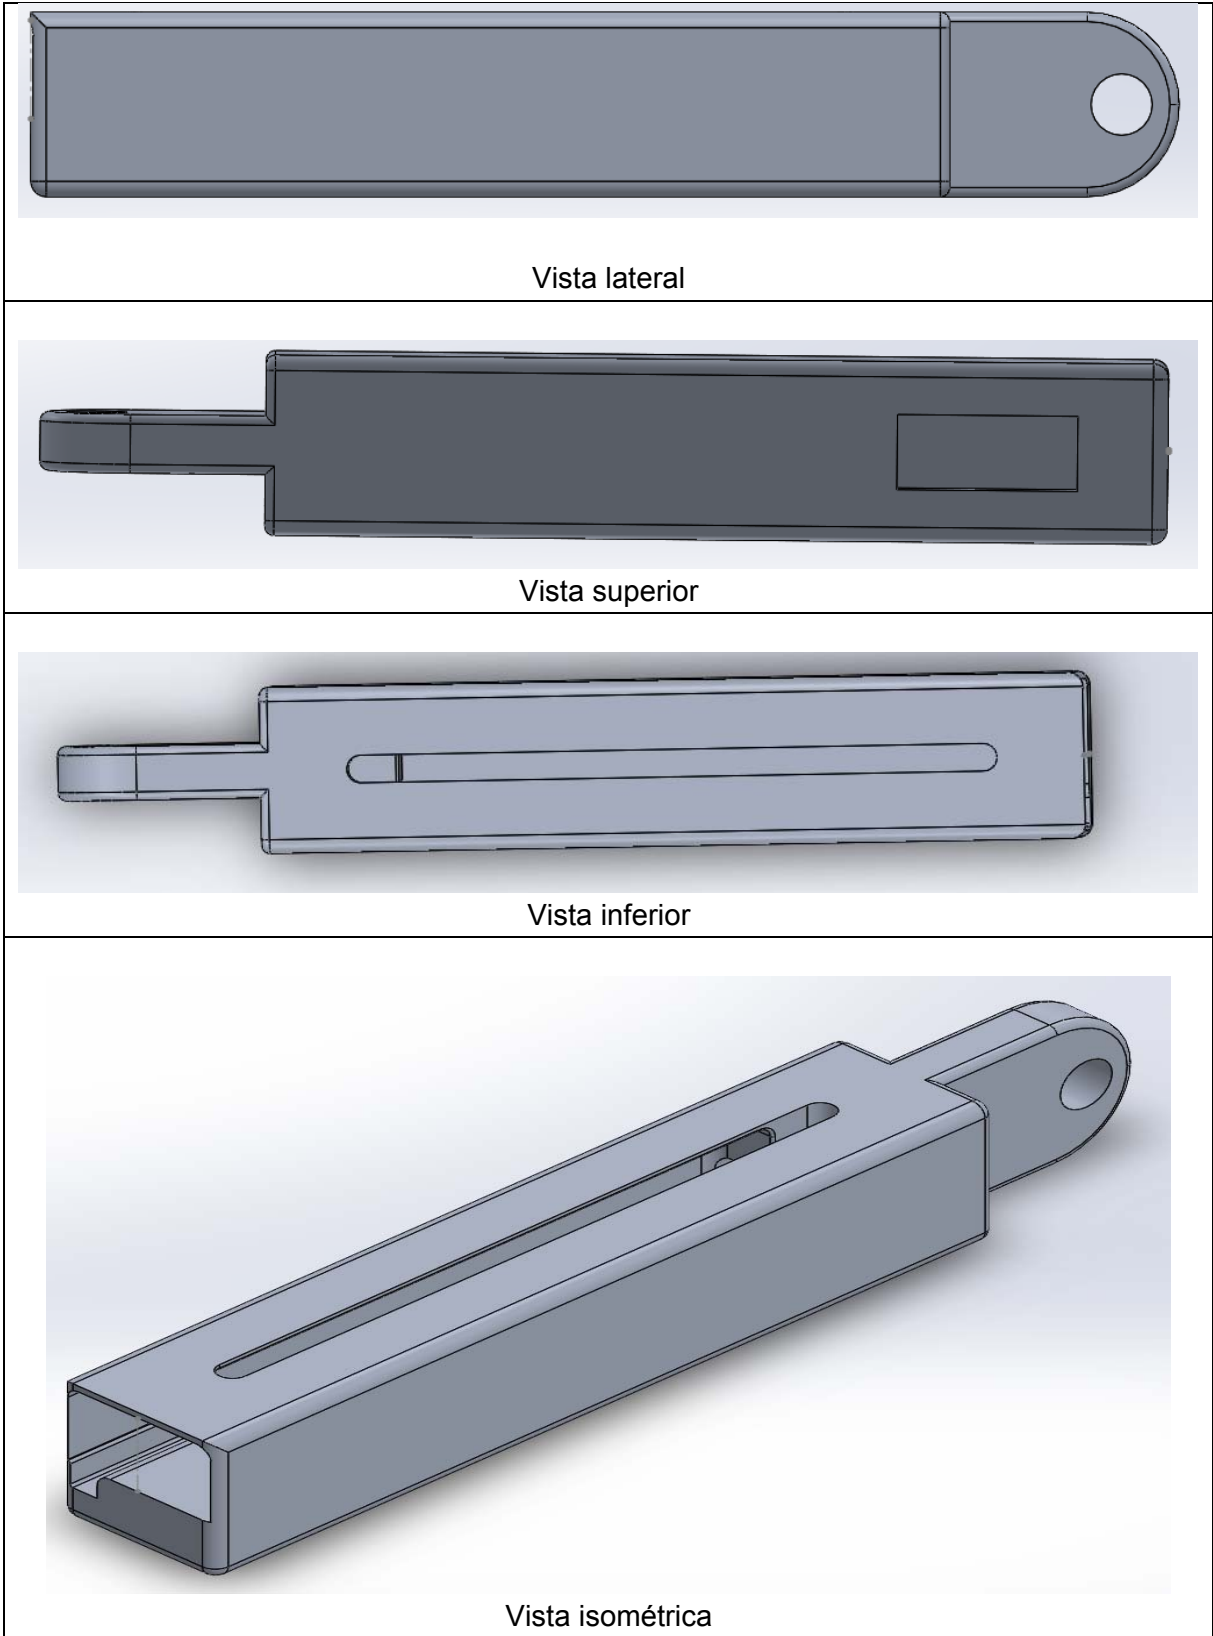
Vista del diseño en Solidworks de la extensión vertical telescópica
